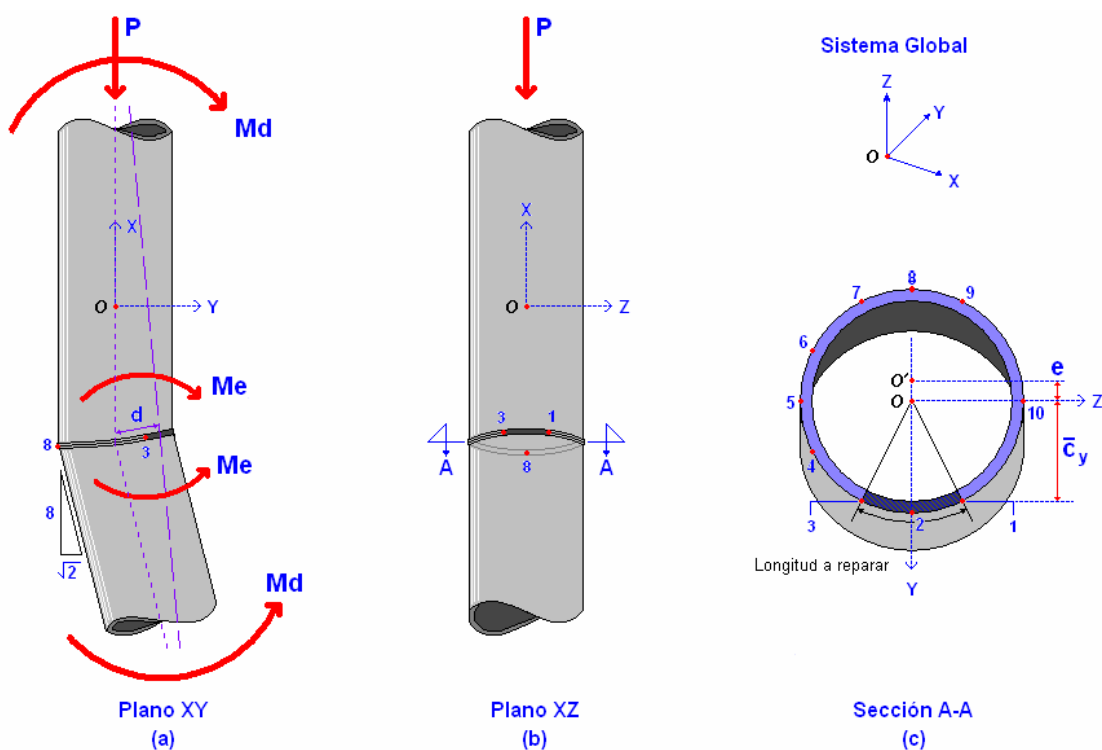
Reparación de soldadura en el cambio de pendiente, en la parte interna.
